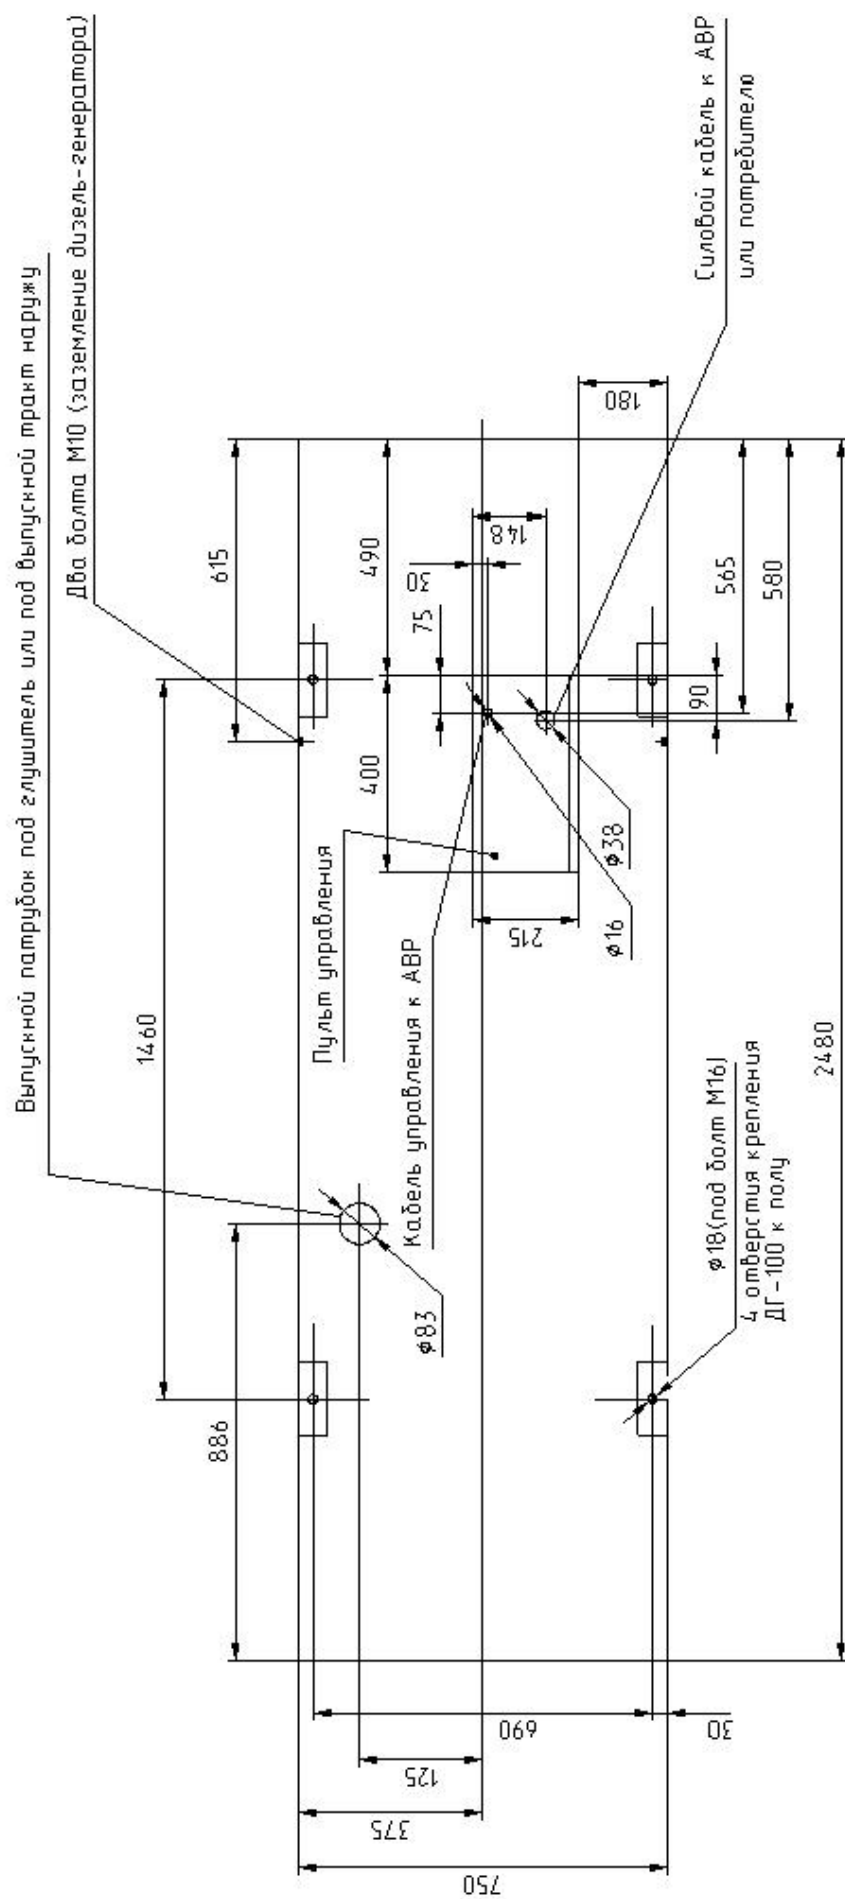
Монтажный чертеж установки ДГ-80/100/125 (вид сверху).
